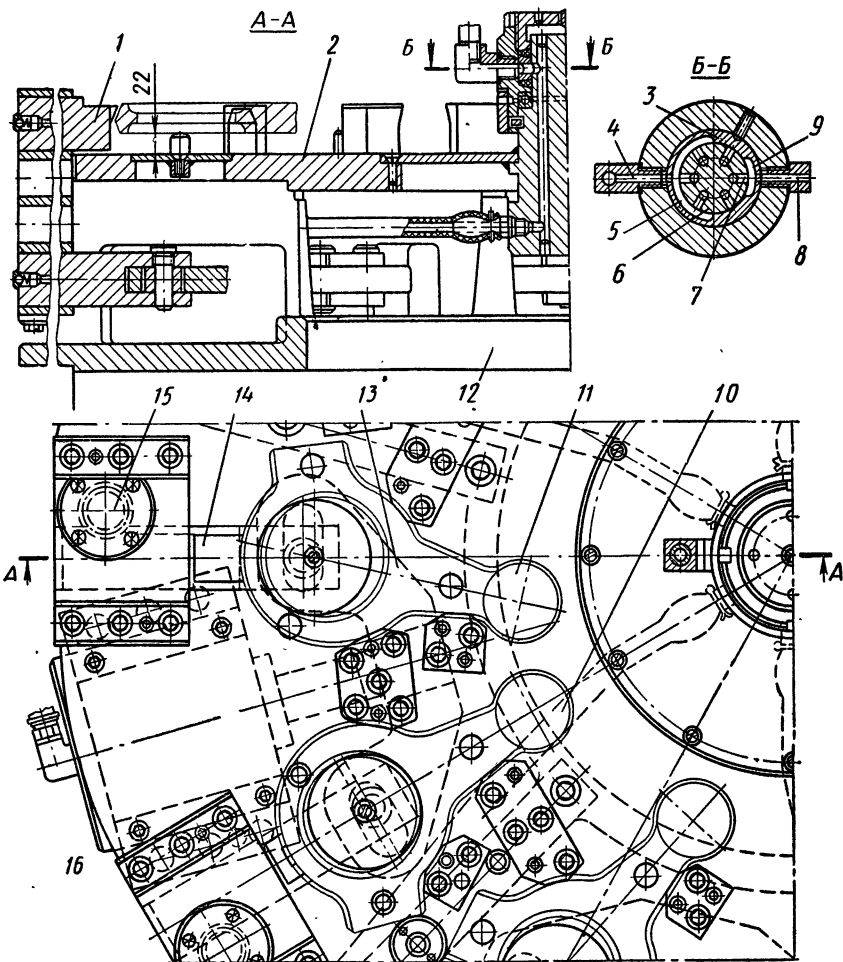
Приспособление с автоматическим креплением деталей при непрерывном фрезеровании
